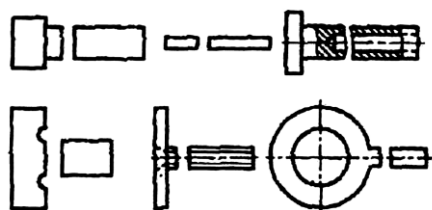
Типы сварных соединений, выполняемых стыковой сваркой сопротивлением
